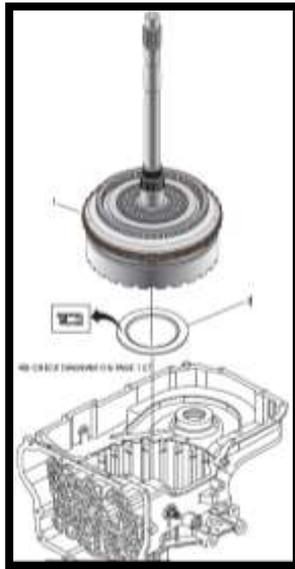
Instalación del tambor de embrague 3-5-R/4-5-6
